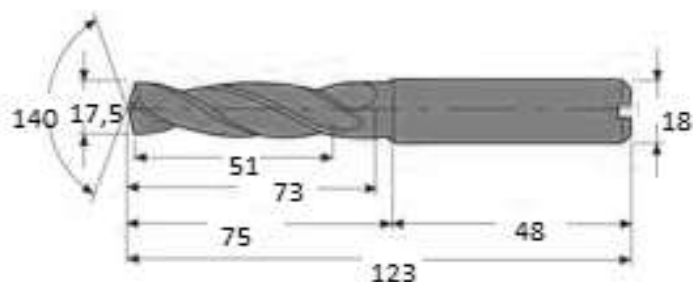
Сверло SD1103A-1750-051-18R1
